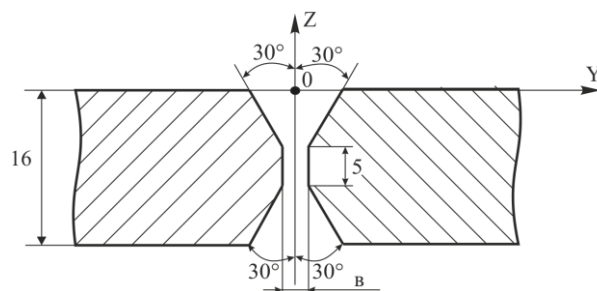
Схема разделки кромок для сварного соединения типа С25.
